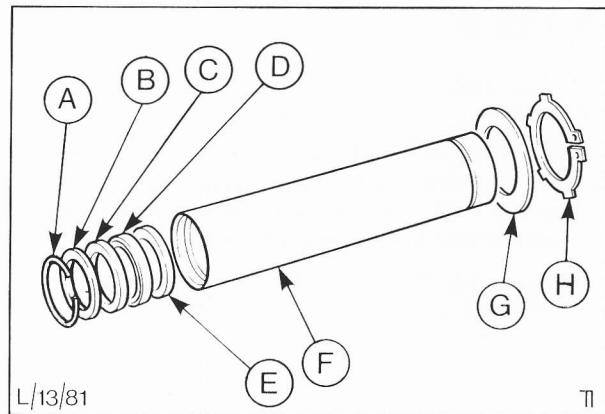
Einbaufolge der Dichtungen und Sprengringe
